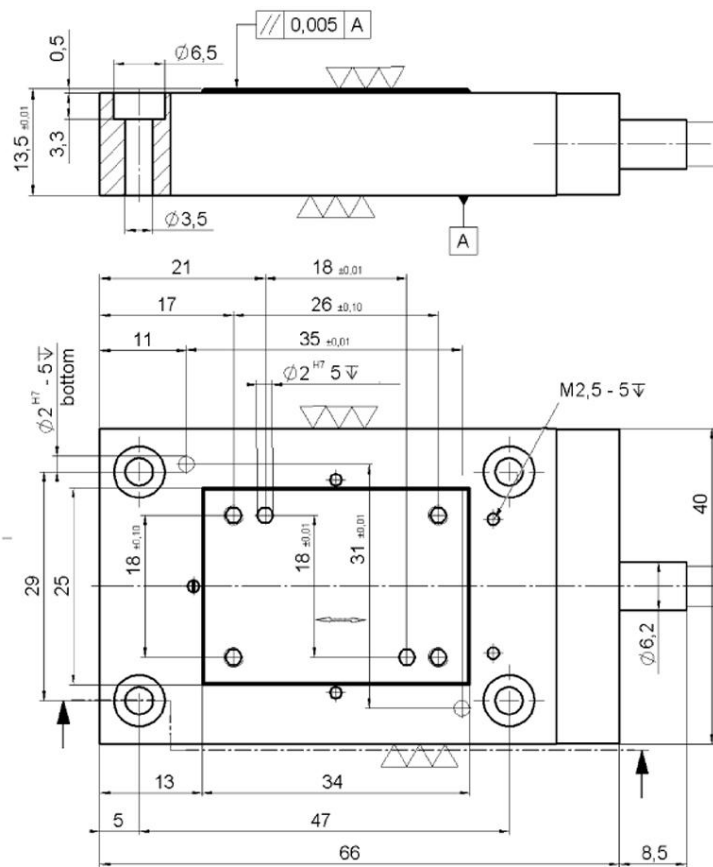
Габаритный чертёж P-752.1xx. Размеры указаны в мм.
